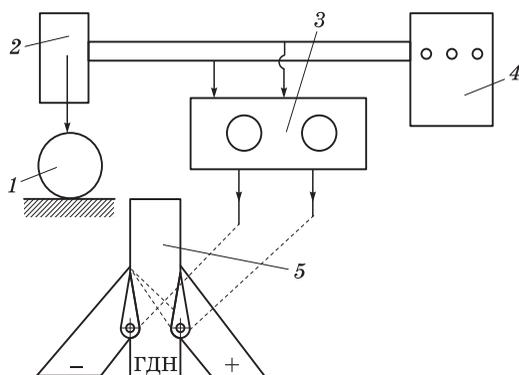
Схема пассивного контрольно-сортировочного устройства
